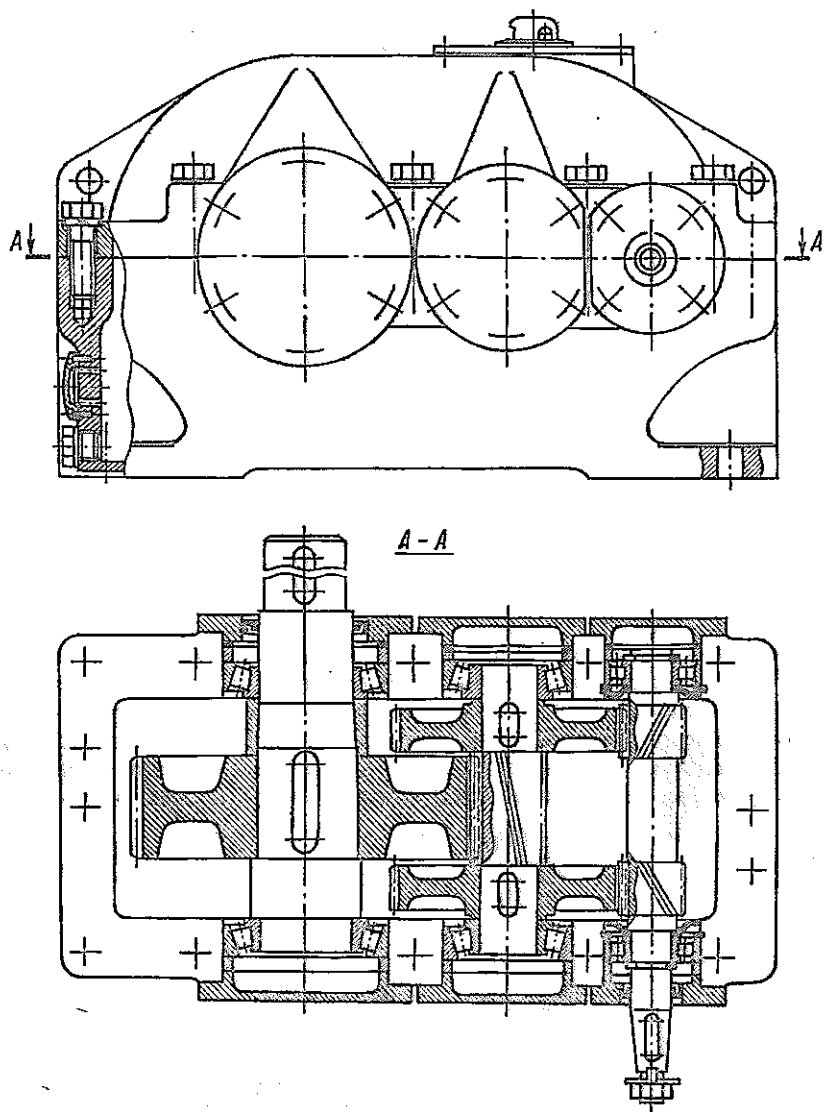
Цилиндрический двухступенчатый редуктор с раздвоенной быстроходной ступенью
